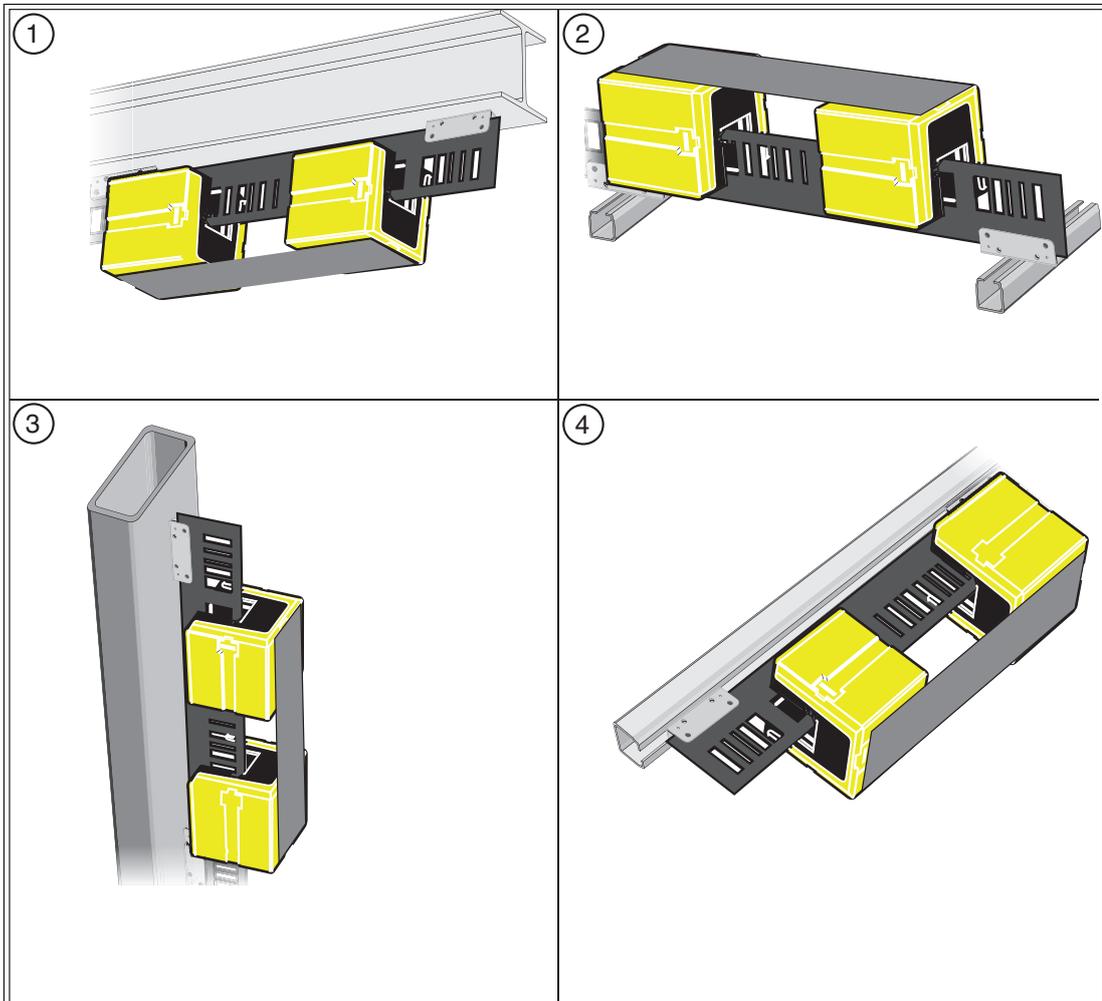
Einbaulagen mit Befestigungswinkeln (Einbaulagen gilt ebenso für die Montage mit dem Aluminium-Profilsystem)
